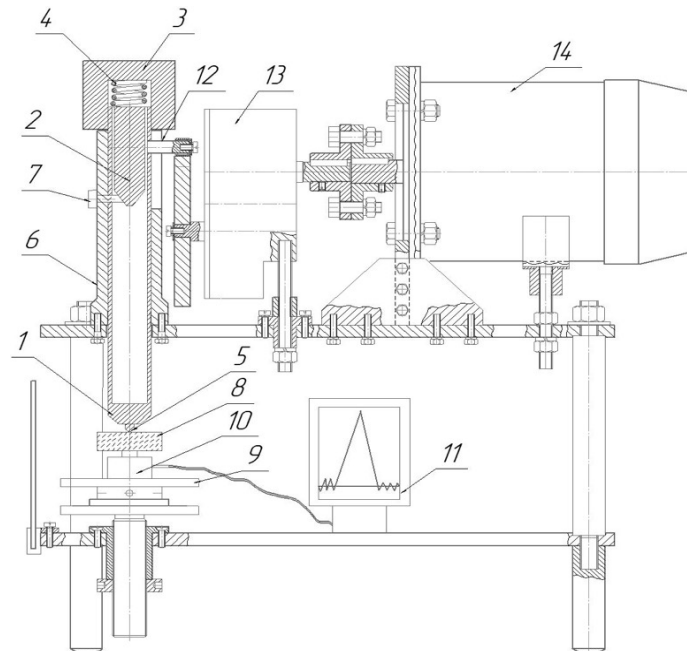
Принципиальная схема установки по разрушению анализируемых материалов: 1 – корпус модельного инструмента; 2 – вставка; 3 – крышка; 4 - пружина; 5 – индентор с полусферической площадкой притупления радиусом $R_m = 3\text{ мм}$; 6 - направляющая труба; 7 - стопор; 8 - пластина породы или металла; 9 – установочная плита; 10 – датчик силы РК 1000; 11 – аналого-цифровой преобразователь NI USB 6008; 12 – кулачок; 13 – редуктор; 14 – электродвигатель.
